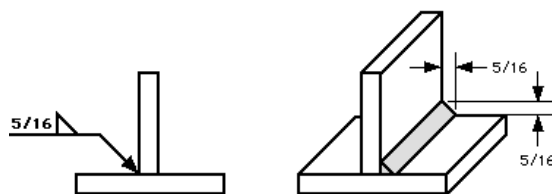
Soldadura de filete (Caras iguales)¹¹
